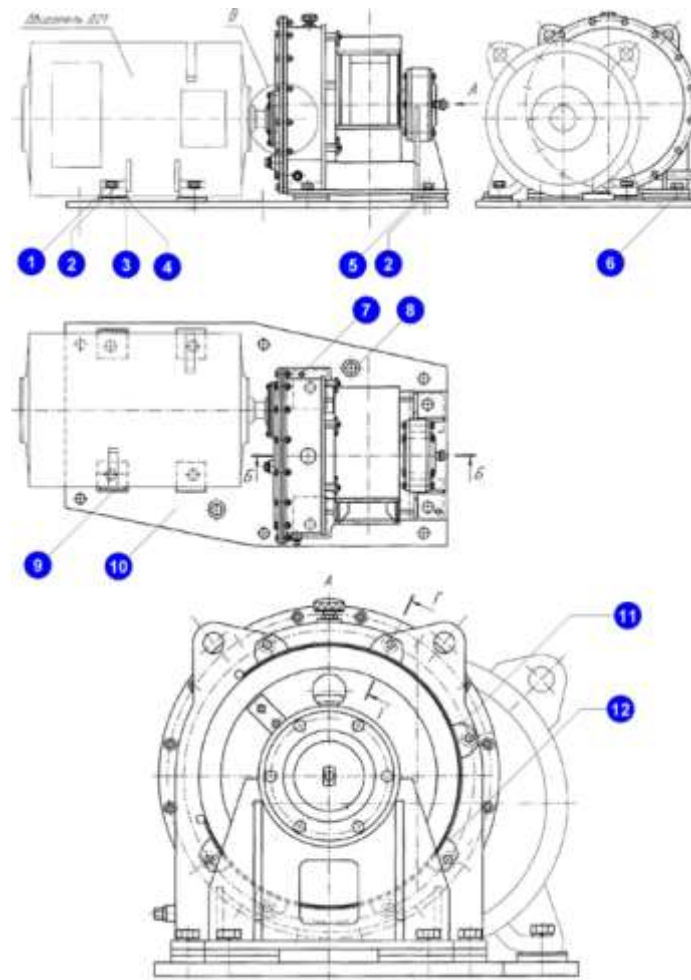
Редукторний механізм відкривання днища ковша [4]
